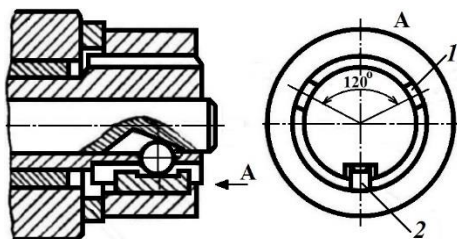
Установочно-разжимная оправка с двумя неподвижными и одним подвижным кулачком
